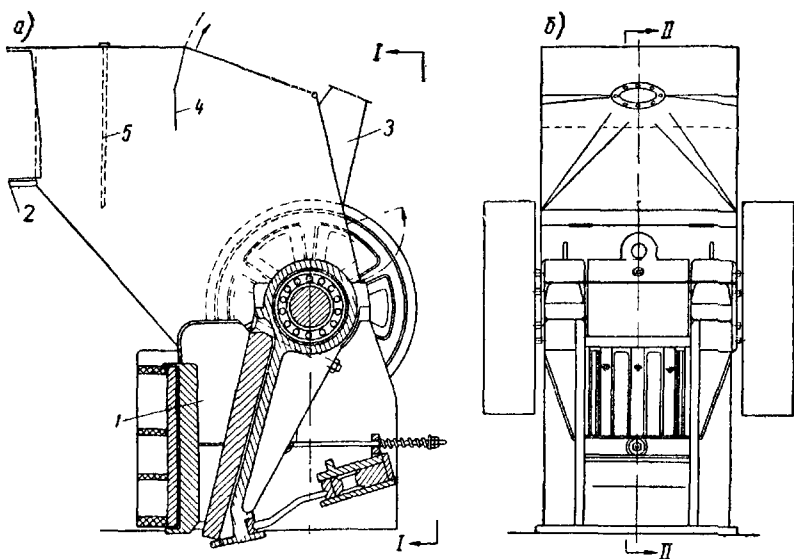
Укрытие щековых дробилок типов ЩЭС и СМ
